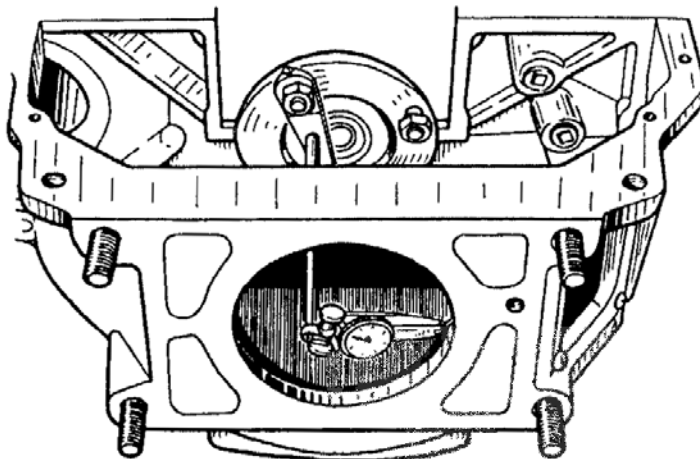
Проверка concentричности установочного отверстия в картере сцепления относительно оси коленчатого вала
